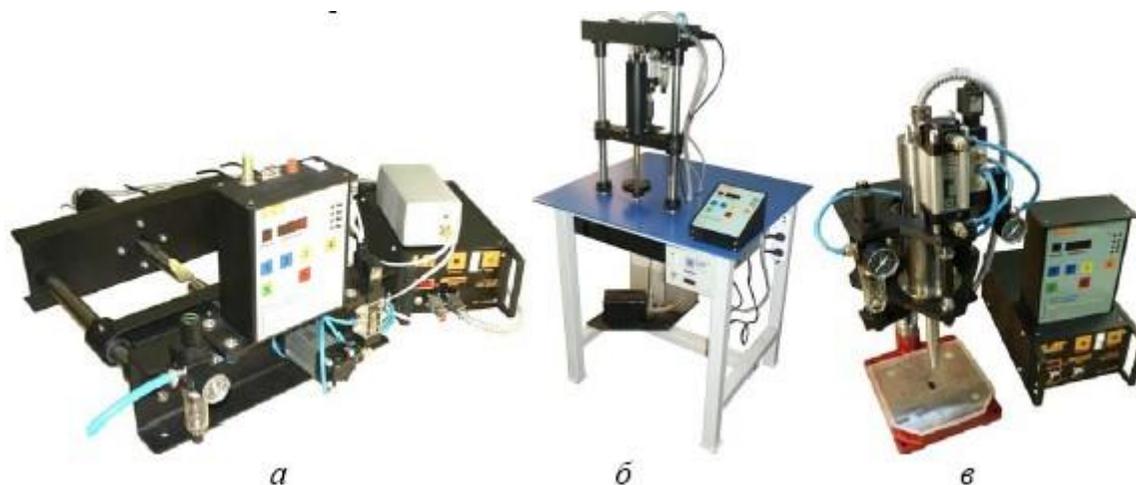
Различные комплектации ультразвукового сварочного пресса ИЛ100-7
